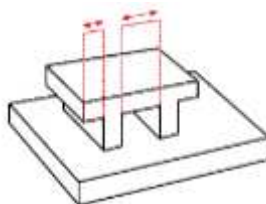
Smjernica za oblikovanje 3D printanih dijelova (4) [16]
